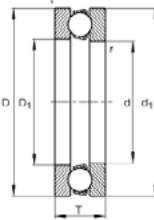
Plano rodamiento axial. Fuente: Schaeffler.
